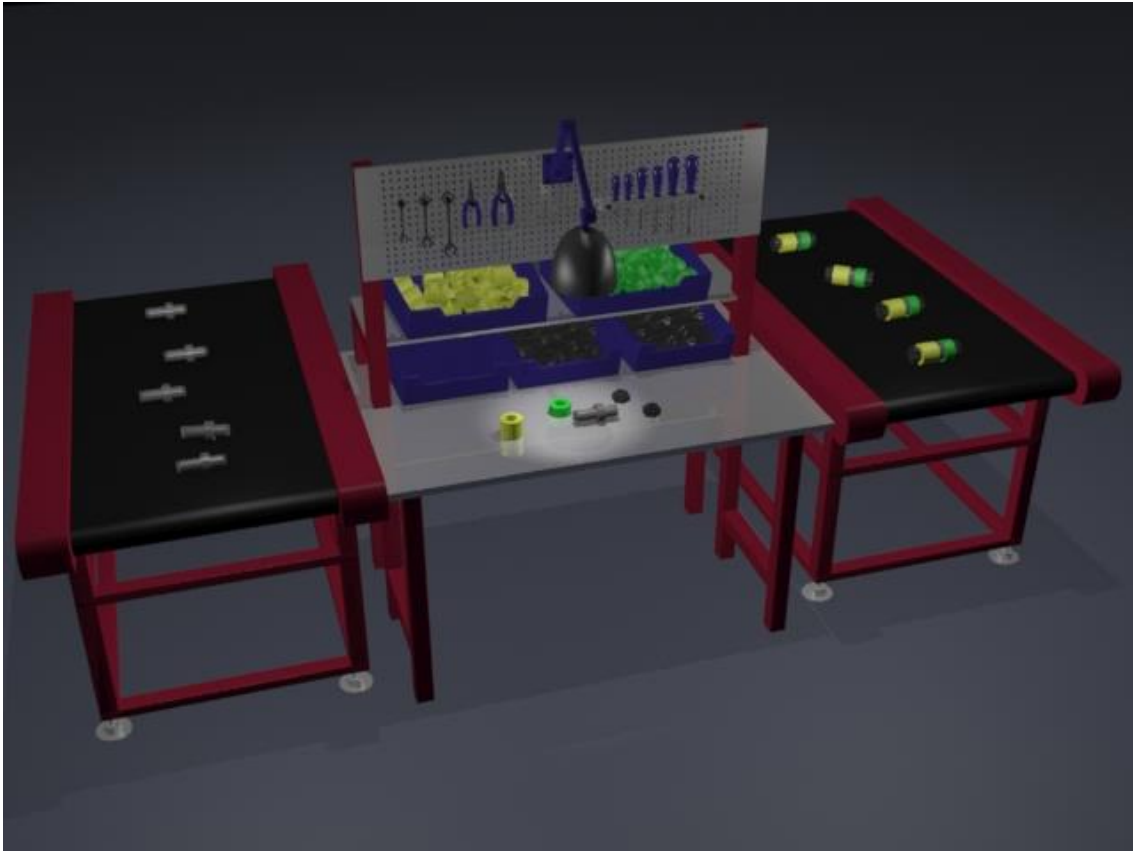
Diseño final del puesto de trabajo de cadena de montaje
